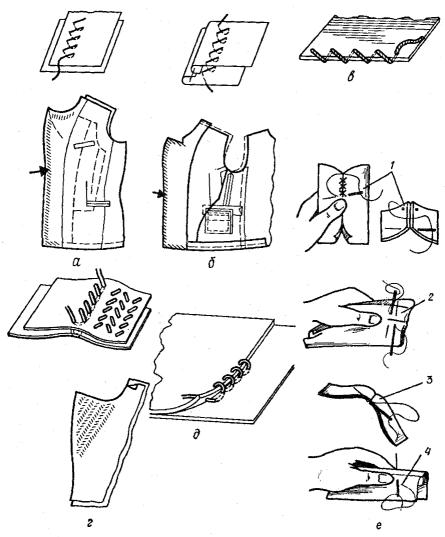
Строчки, образованные с помощью косых стежков: a — наметочная; b — выметочная; s — обметочная; c — стегальная; d — подшивочная; e — для незаметного скрепления деталей: l — d — штуковка, d — распошивка.
